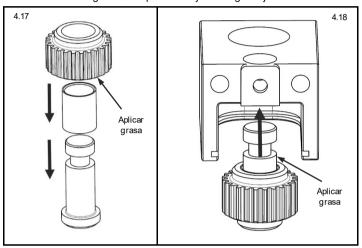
Engrasar y montar el engranaje intermedio Fig. 4.18 Introducir el engranaje intermedio
